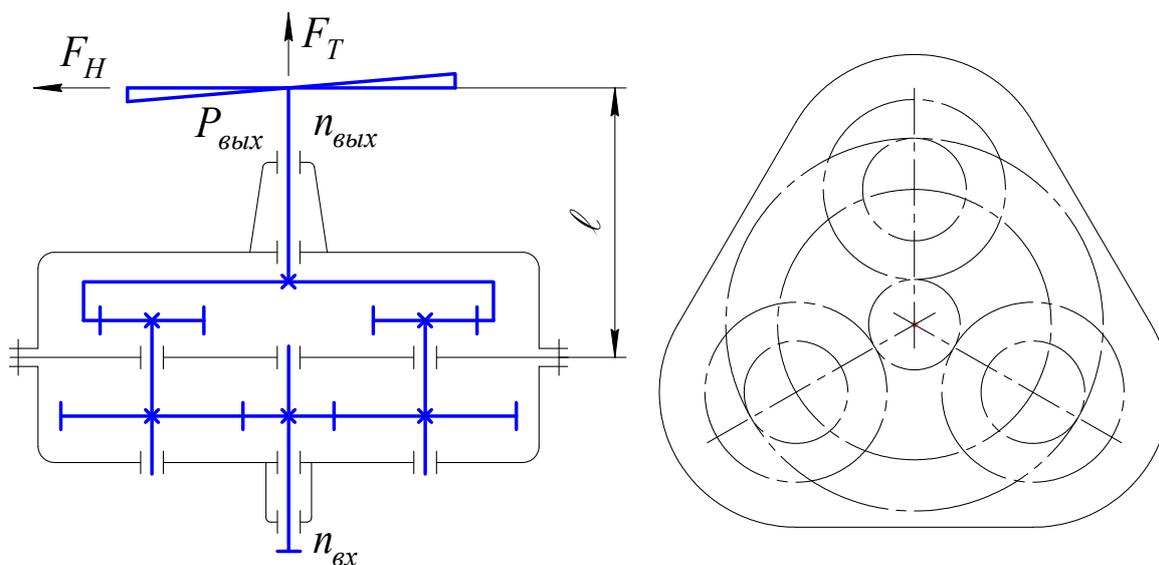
Схема соосного многопоточного цилиндрического редуктора
